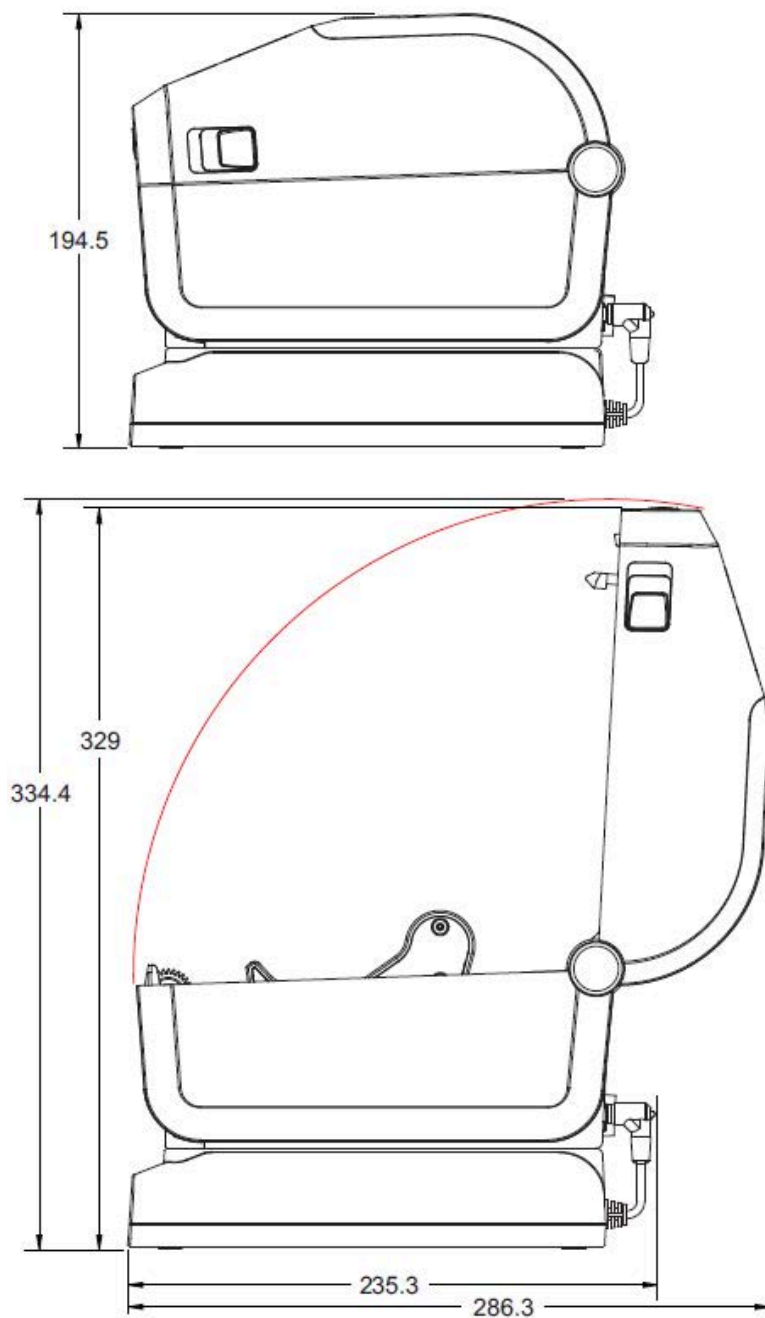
Принтер для прямой термопечати — стандартный и с дополнительными модулями резака и отделителя
